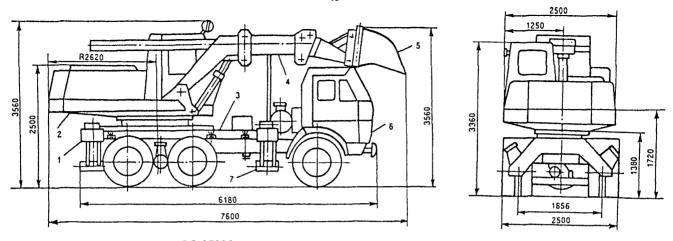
Общий вид экскаватора ЭО-3532A: 1, 7 - выносные опоры; 2 - поворотная платформа; 3 - накладная рама; 4 - телескопическое рабочее оборудование; 5 - ковш; 6 - базовое шасси КамАЗ-5511
